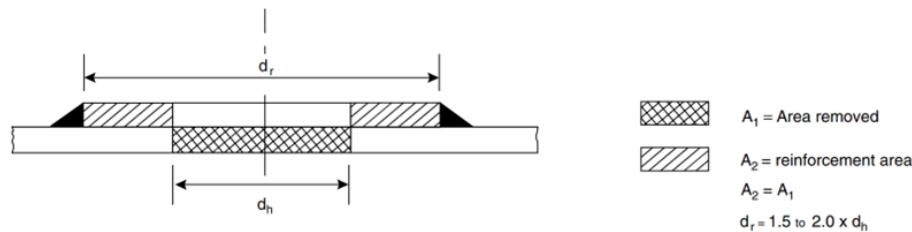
Método de áreas iguales para la abertura de asiento soldado (9)
